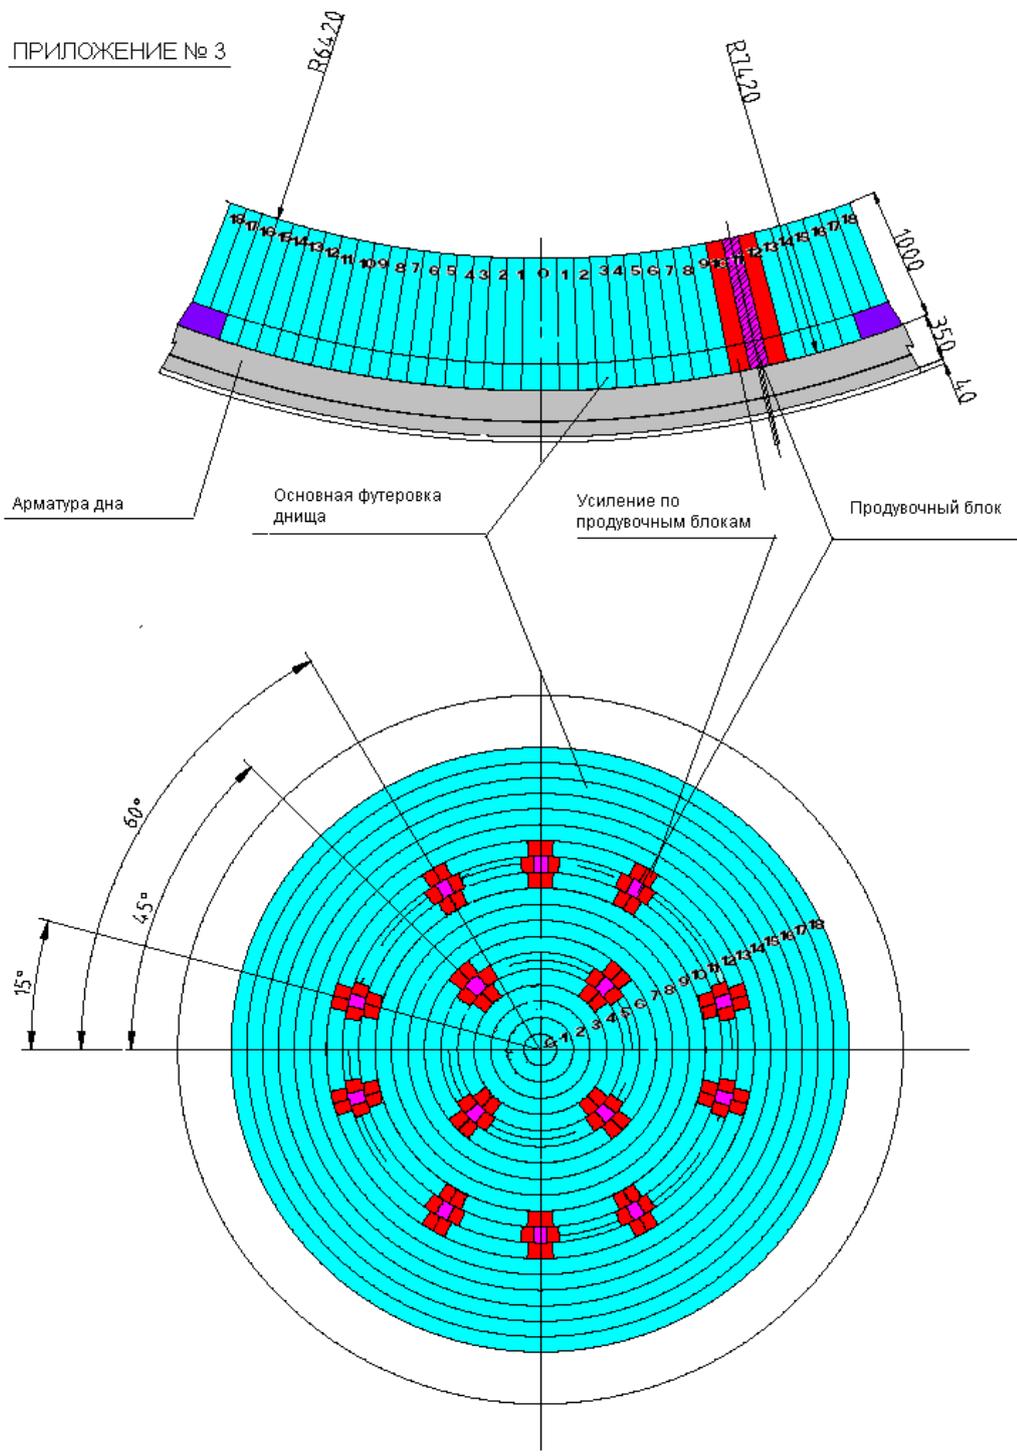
Расположение продувочных блоков в днище конвертера (вид сверху)
